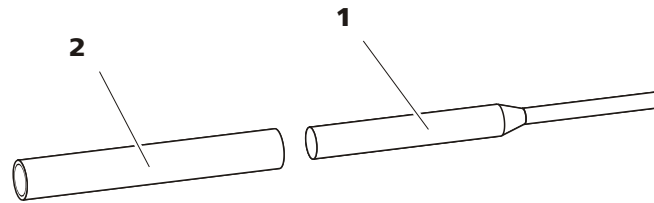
Werkzeug für Kolbendichtung 6.2617.010
